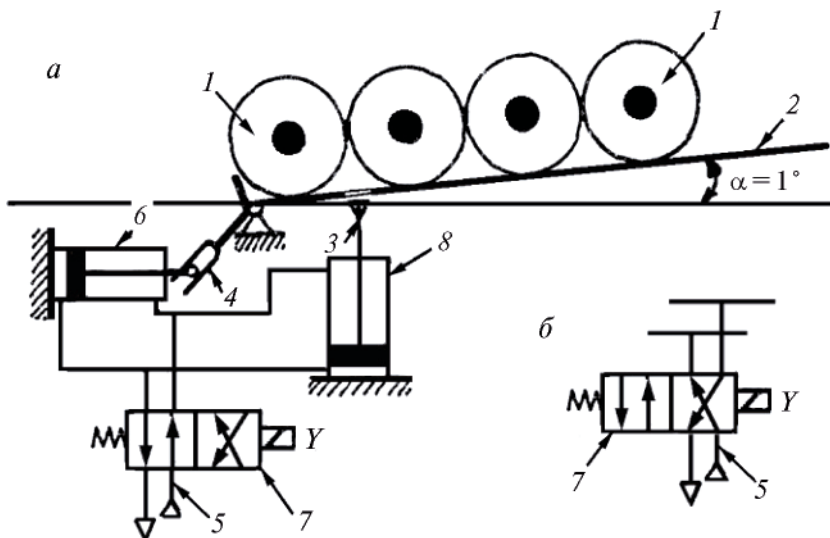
Конструктивная схема загрузочного устройства для подачи колесных пар:
